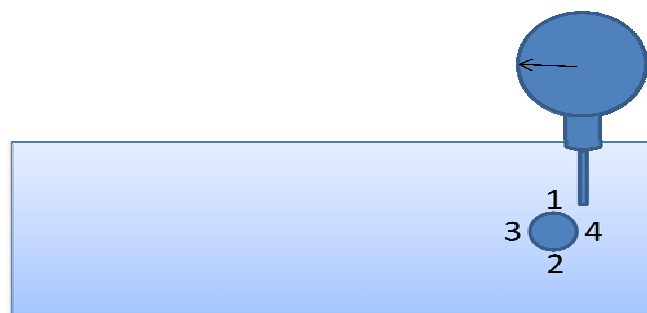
Esquema da medição das indentações nas chapas soldadas.
